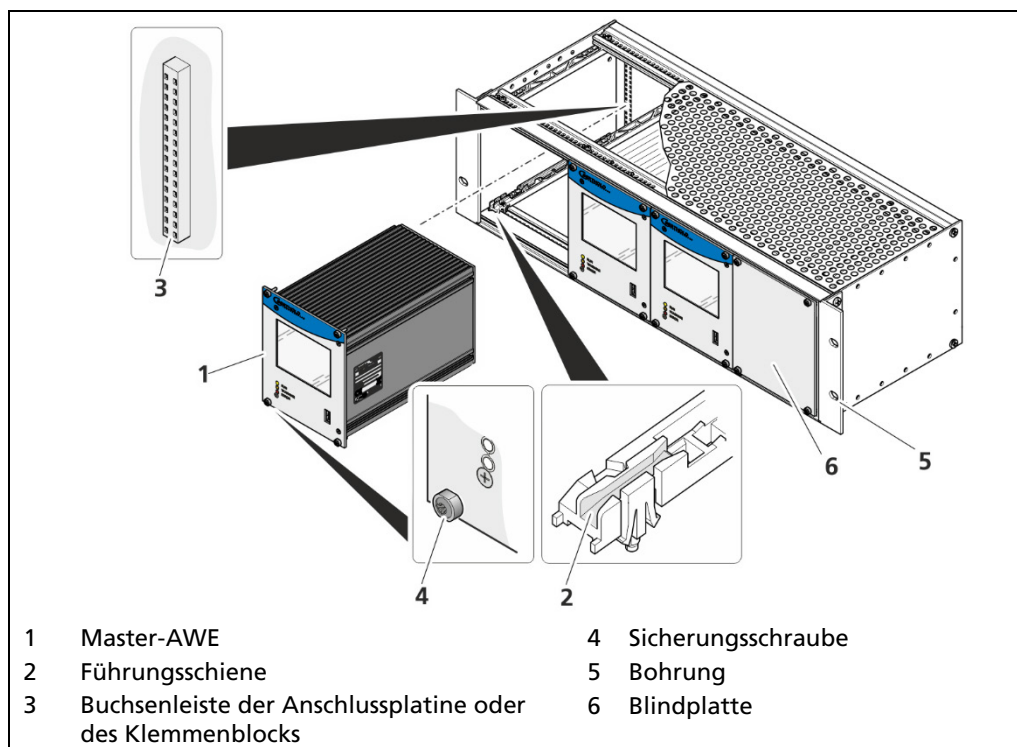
19"-Baugruppenträger mit Klemmenblöcken (Beispiel: 3x Master)
